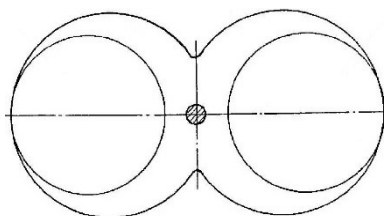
Мішалка для рідин (вид зверху; пат. RU2048876C1)
